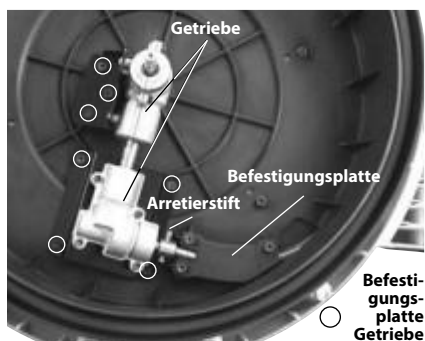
Geöffnetes Gehäuse der Abflussreinigungsmaschine
